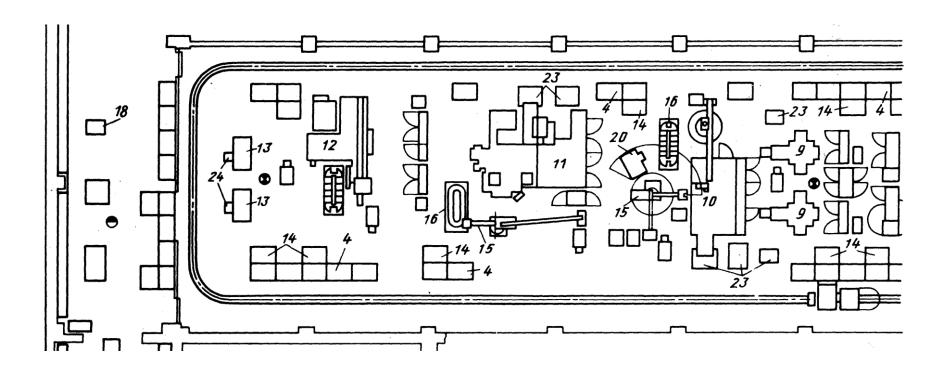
Планировка ГПС ACB-201 для изготовления деталей типа тел вращения в мелко- и среднесерийном производстве (левая часть)
